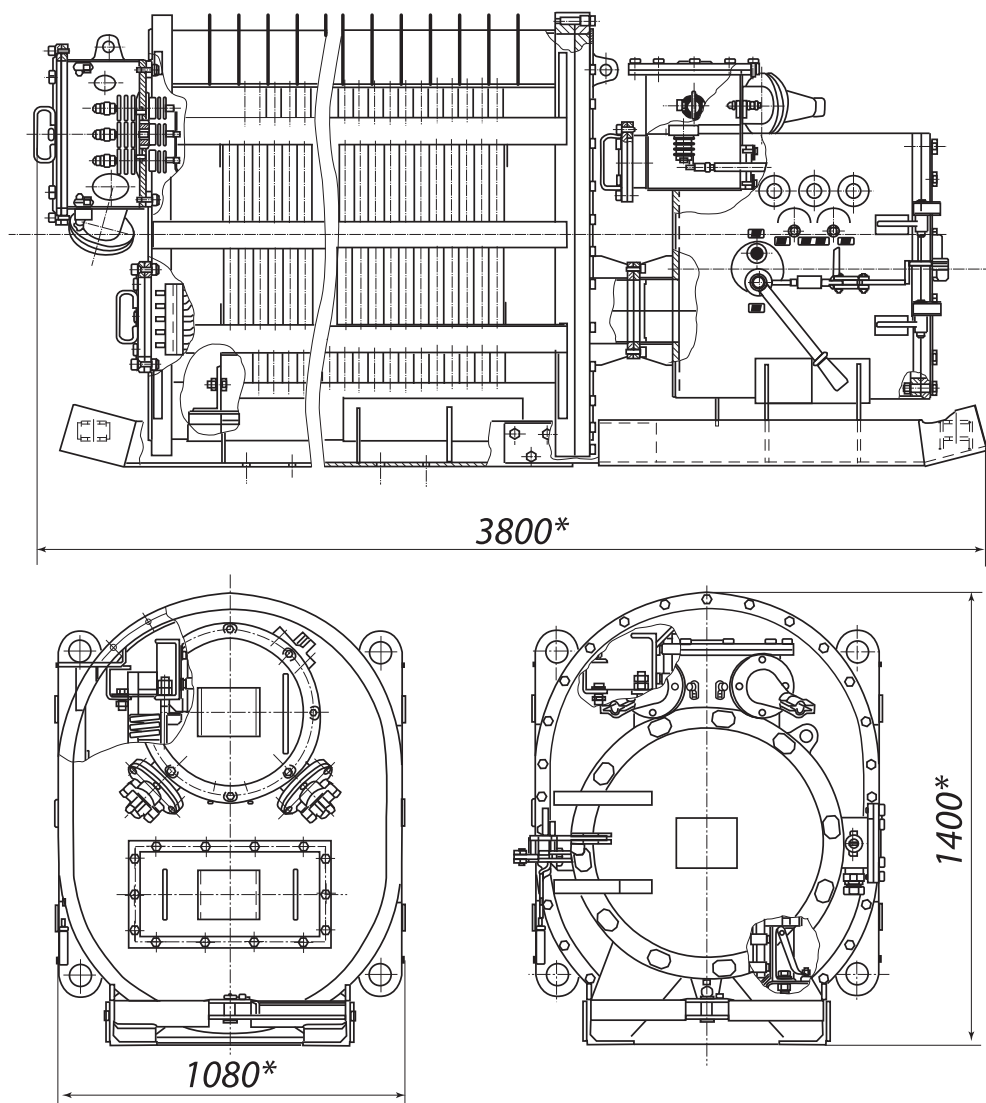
Общий вид и габаритные размеры подстанций типа ВСПП-КРУ
